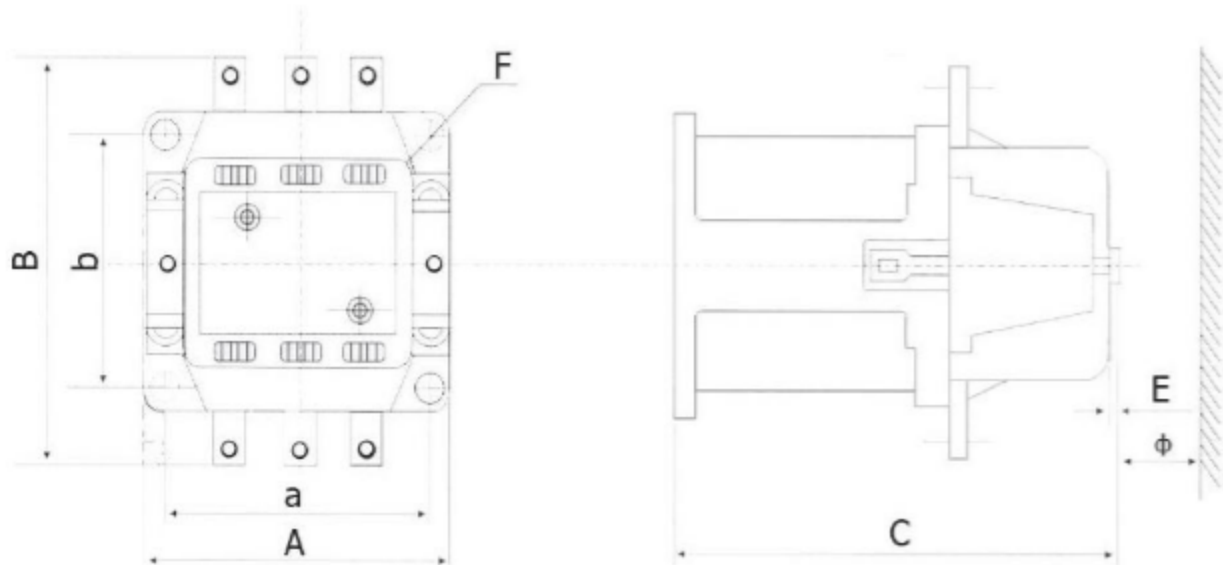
Габаритные и присоединительные размеры пускателей 100-250А
